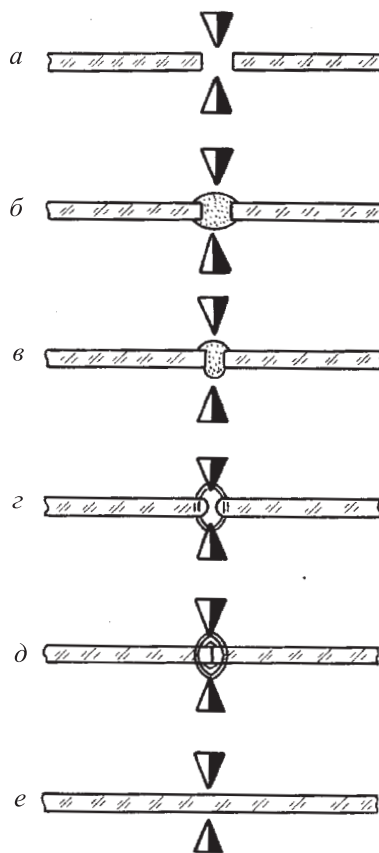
Технологический процесс сварки световодов: *a* — начальное состояние; *б* — введение смеси; *в* — сближение; *г* — оплавление торцов; *д* — сближение и сварка; *е* — окончание сварки
